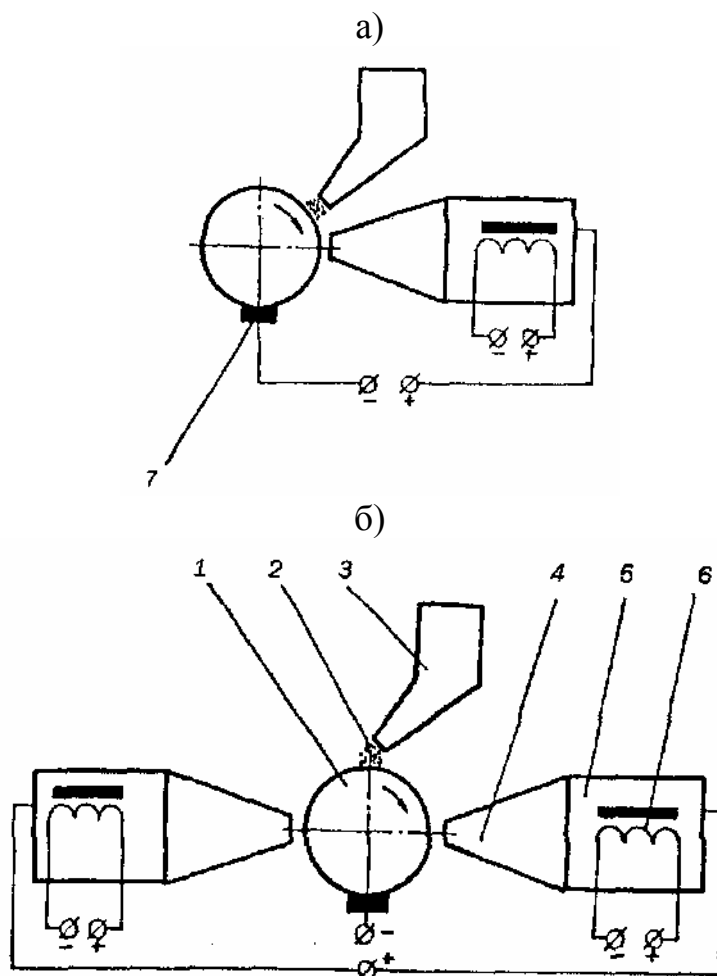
Схема установки для электромагнитной наплавки: а) – однополюсной; б) – двухполюсной; 1 – заготовка, 2 – порошок, 3 – бункер, 4 – наконечник, 5 – корпус, 6 – электромагнит, 7 – щетка
